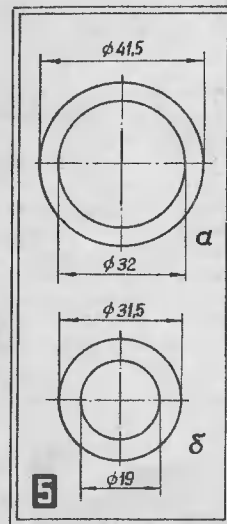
Регулировочные шайбы: а — вторичного вала; б — промежуточного вала.
